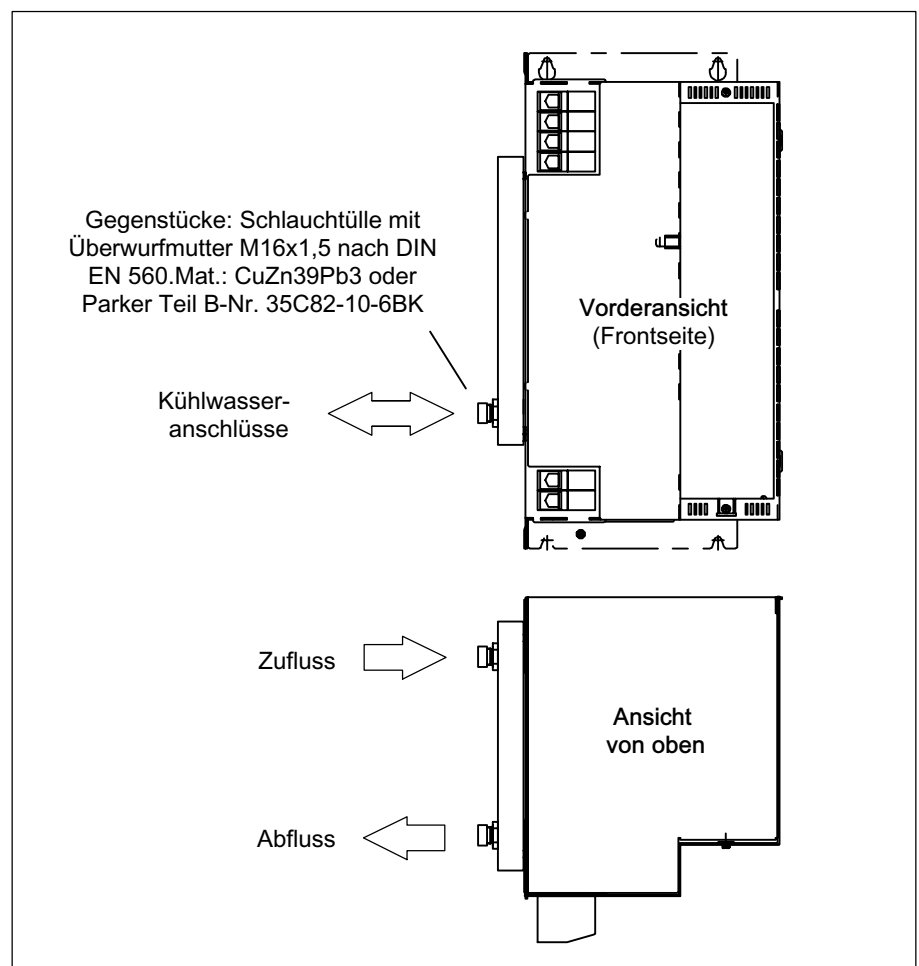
Position Kühlwasseranschluss: PSI 6300/63C0.xxx Wx
